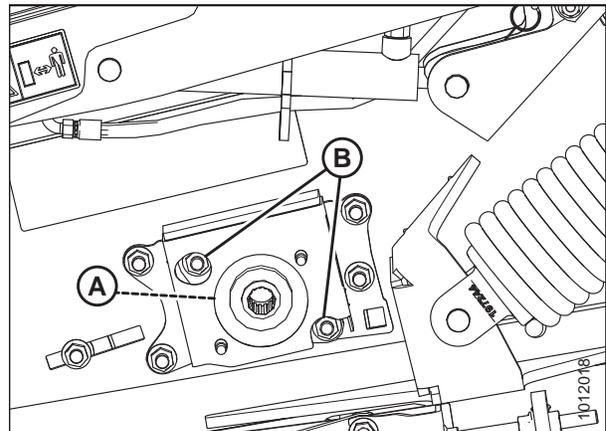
Rodillo de mando de la cama frontal del lado izquierdo
